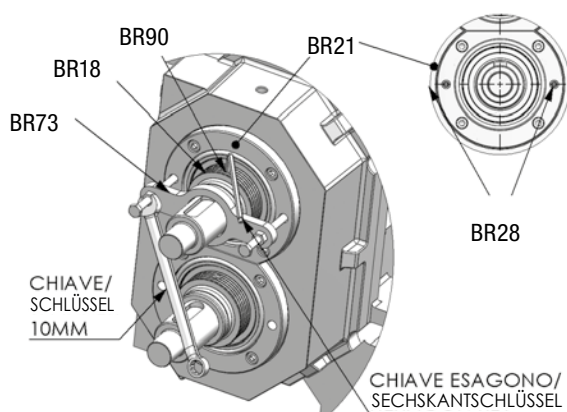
Montage der mechanischen Dichtungen (Phase 2).
